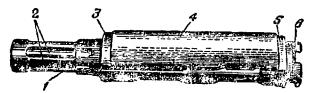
Газовая трубка со ствольной накладкой: I— газовая трубка; 2— направляющие ребра для газового поршия; 3— передняя соединительная муфта: 4— ствольная накладка; 5— задия соединительная муфта; 6— выступ
